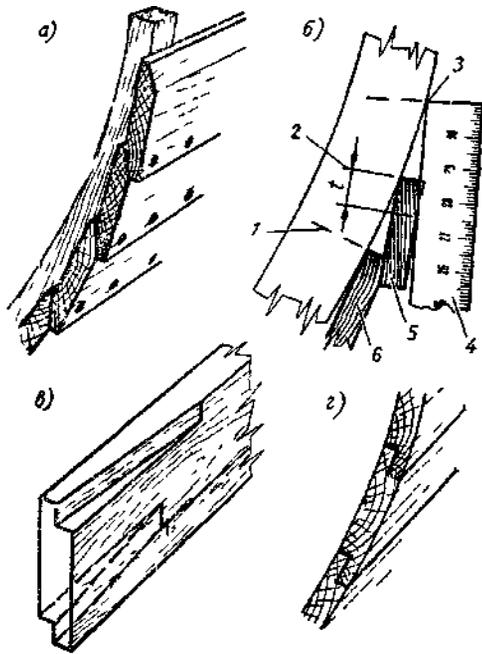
Обшивка типа внакрой: а — конструкция обшивки; б — разметка малки на верхней кромке пояса; в — разметка кромок пояса у форштевня и транца; г — крепление обшивки на транце.
